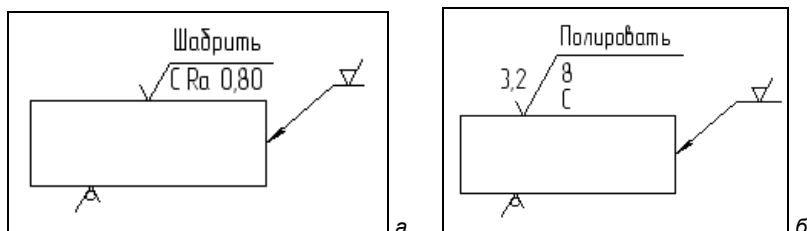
а — пример простановки обозначений шероховатости с изменением № 3; б — пример простановки обозначений шероховатости в редакции Предыдущая
